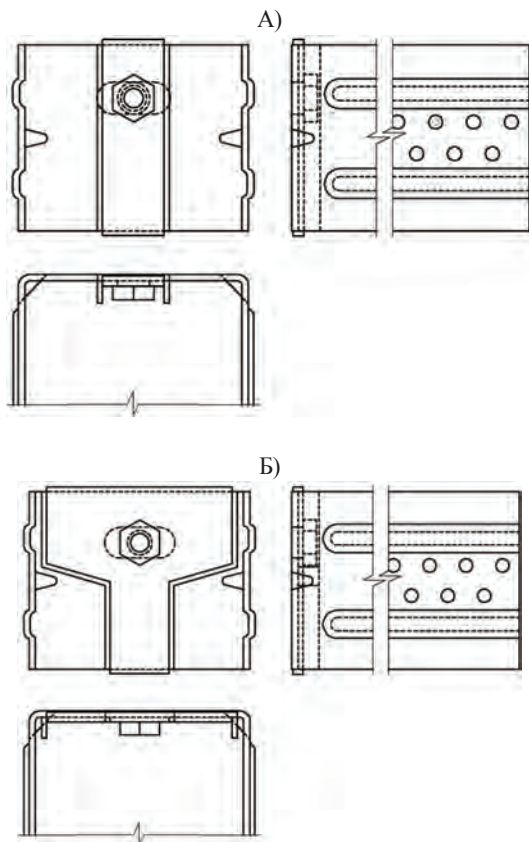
А. Несущий стеновой кронштейн со стандартной усиливающей шайбой в сборе;
